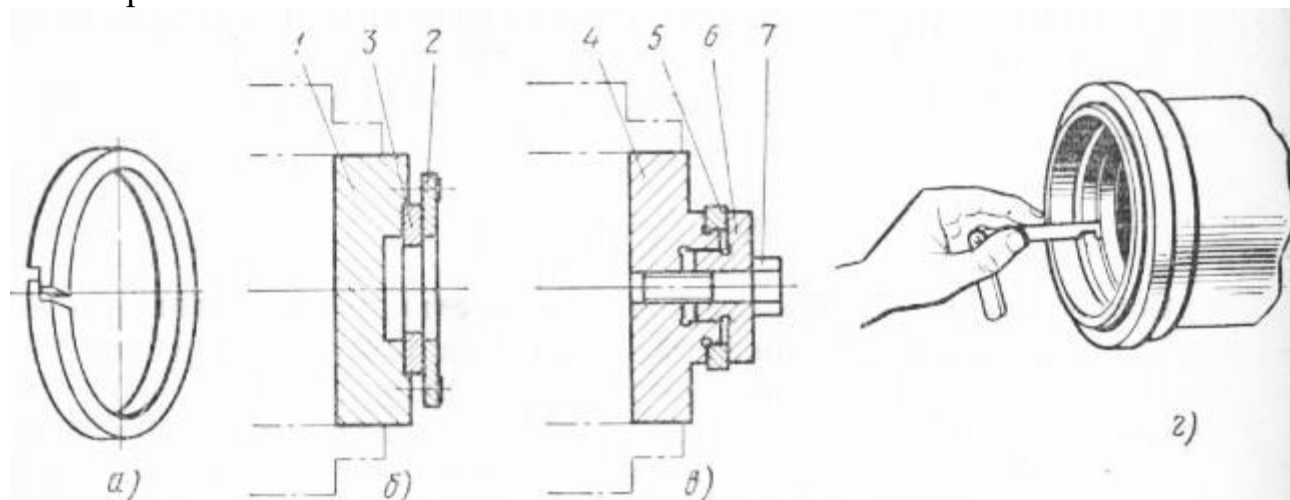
Поршневые кольца: а — форма замка кольца, б — схема закрепления заготовки кольца для обработки по внутреннему диаметру, в — закрепление кольца для обработки по наружному диаметру, г — измерение зазора в замке шупом
